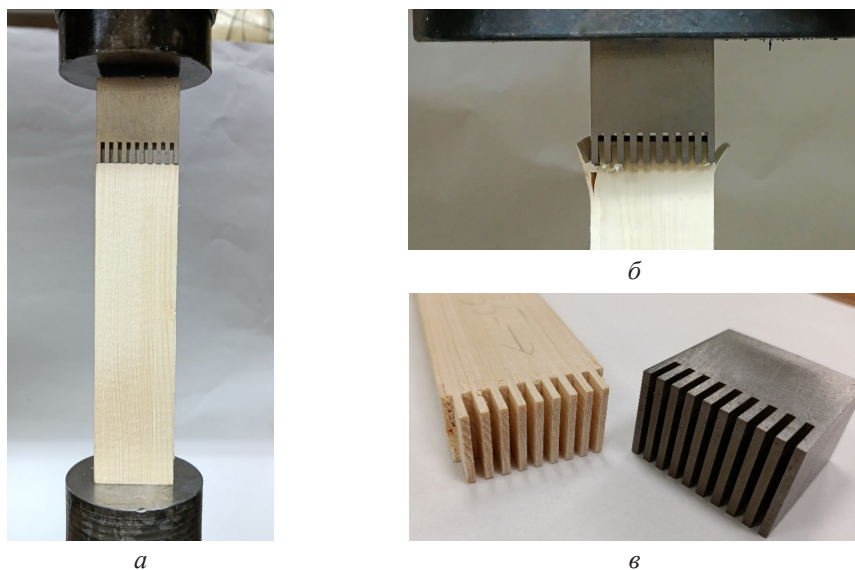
Процесс и результат формирования шипов: а – заготовка и пуансон на столе пресса; б – внедрение пуансона в заготовку; в – внешний вид пуансона и прессованной заготовки
